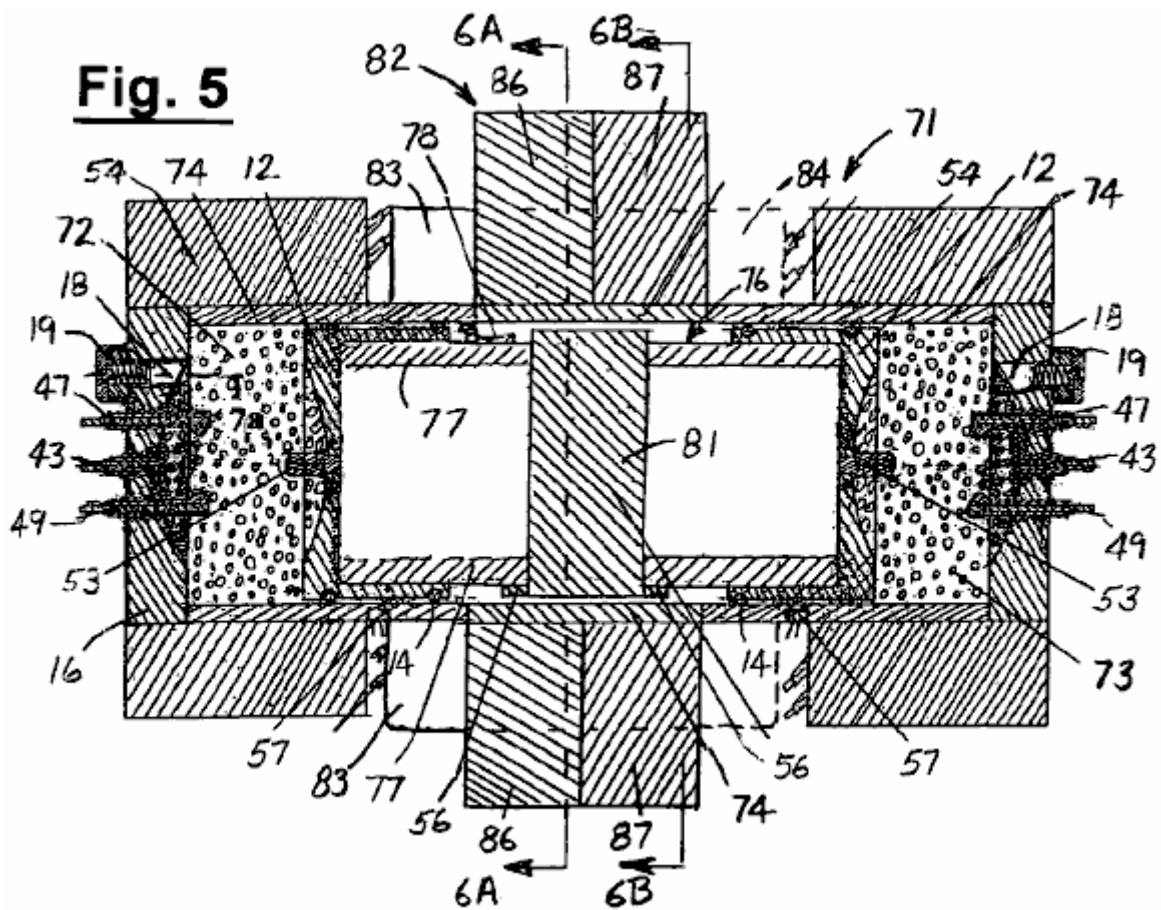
ist eine Mittellinienschnittansicht einer weiteren Ausführungsform eines internen Explosionsmotors und Generators, der die Erfindung beinhaltet.
